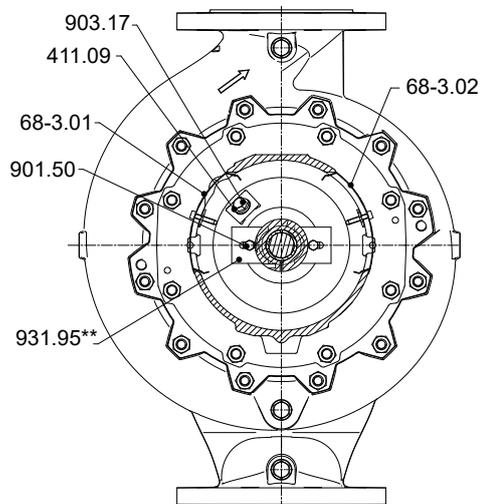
Gesamtzeichnung Seitenansicht ( im Betriebszustand)
